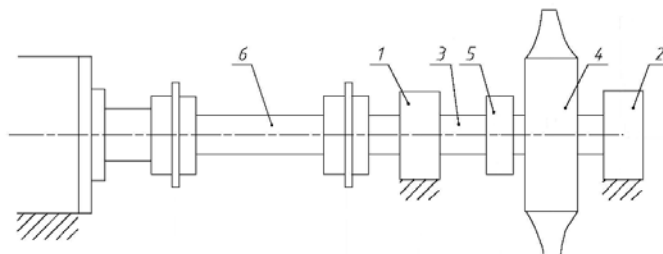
Компоновка ротора по схеме 1 с трансмиссионным валом: 1 – радиальная подшипниковая опора; 2 – радиально-упорная подшипниковая опора; 3 – коренной вал ротора; 4 – рабочее колесо; 5 – исполнительный механизм поворота лопаток РК; 6 – трансмиссионный вал
